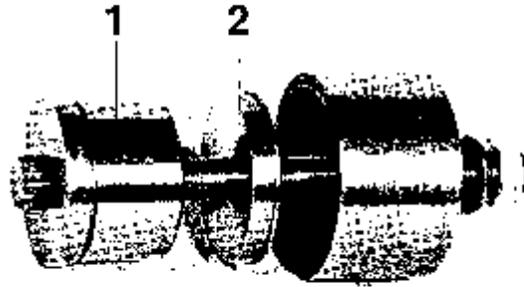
Werkzeug 884489 für Aus- und Einbau der Kurbelwellenlager
